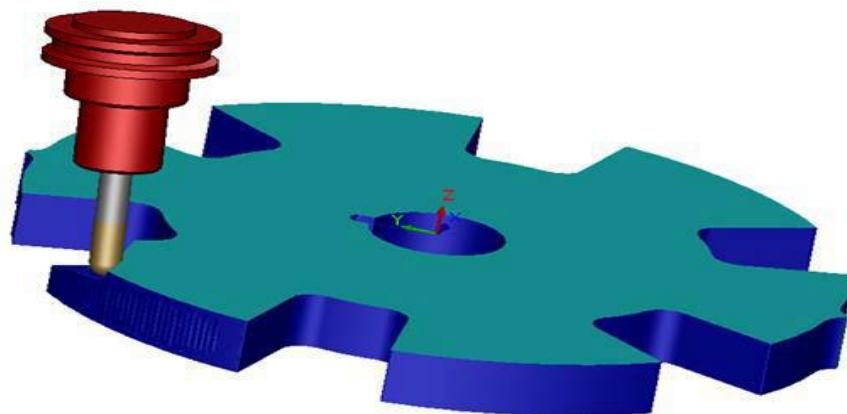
Cambio de herramienta y maquinado de los álabes
